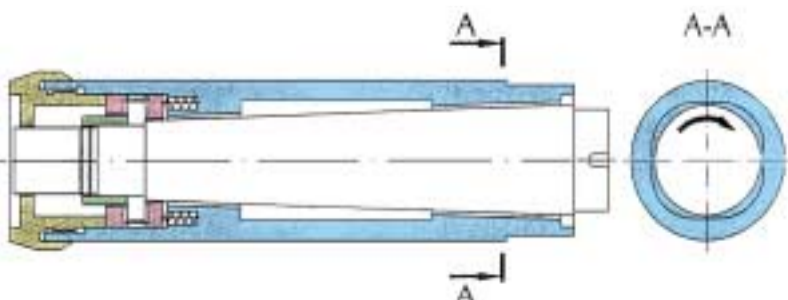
Конструкция гидродинамической опоры бабки изделия.
